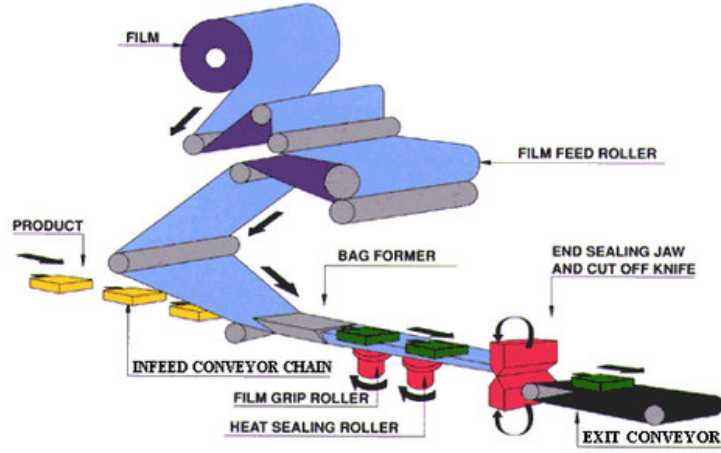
Üstten ambalaj malzemesi beslemede motor kullanımı
